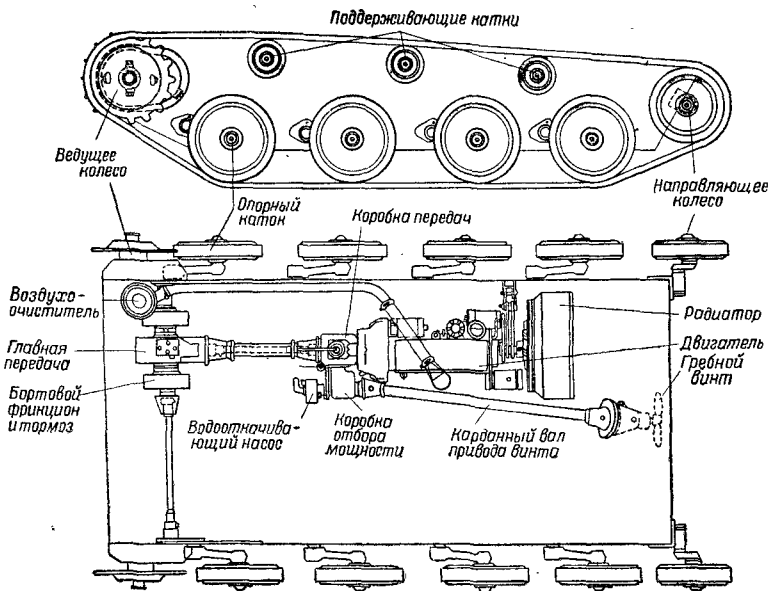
Схема расположения основных агрегатов плавающего танка Т-40
